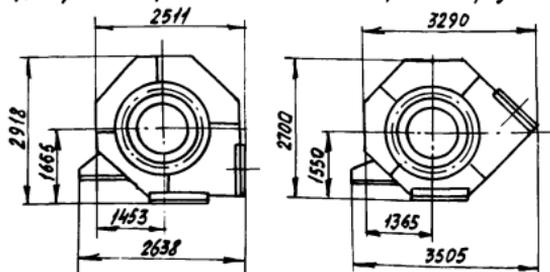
Вентилятор В.Ц4-75-16-01 (исполнение 6) левого вращения. Положения корпусов.
